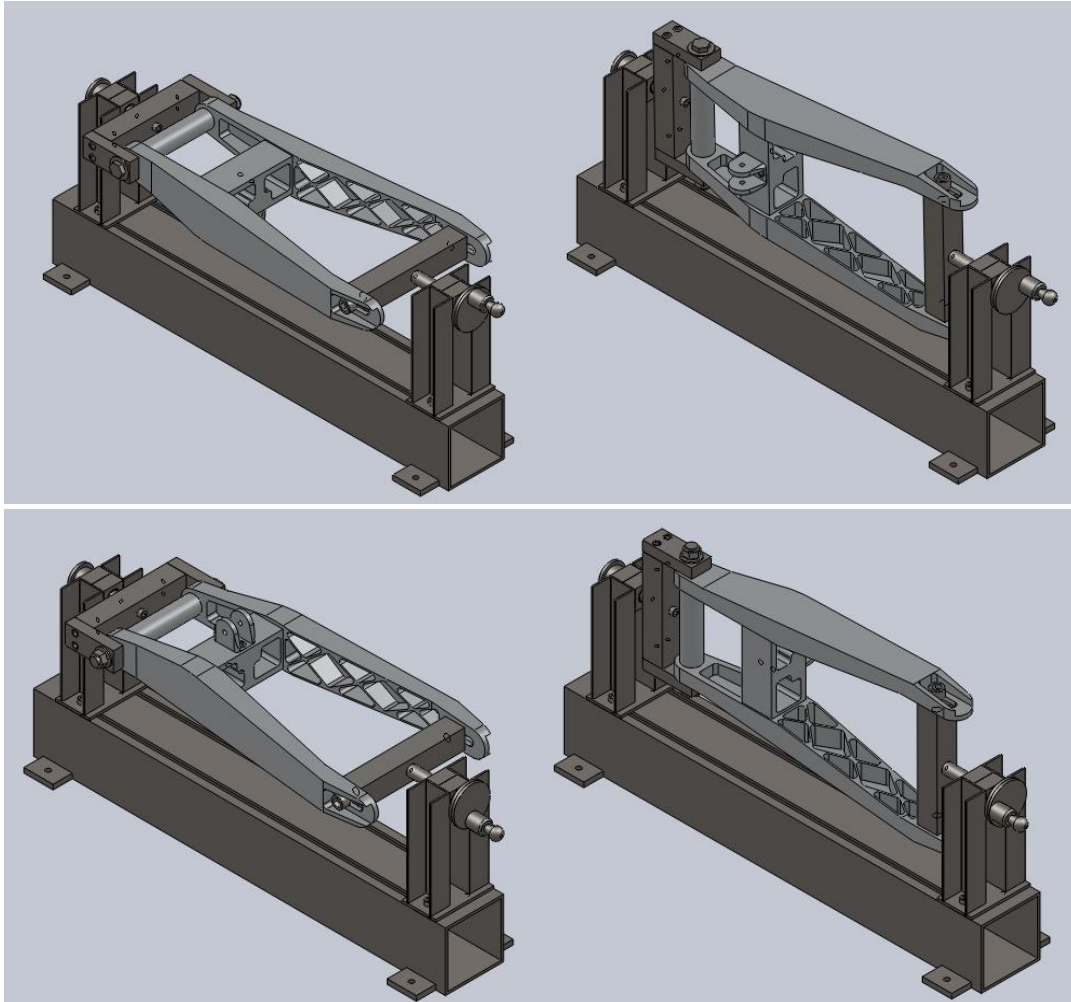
19. Posiciones de soldeo potro de soldadura
